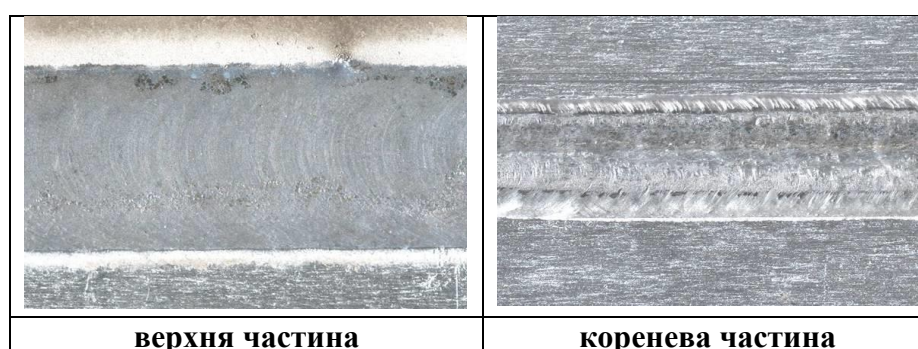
Верхня та коренева частина зварного з'єднання листів товщиною 6 мм сплаву АМгб, сформованого при плазмо-дуговому зварюванні у нижньому положенні з використанням сталеві підкладки з канавкою розмірами 10x2,0 мм.
